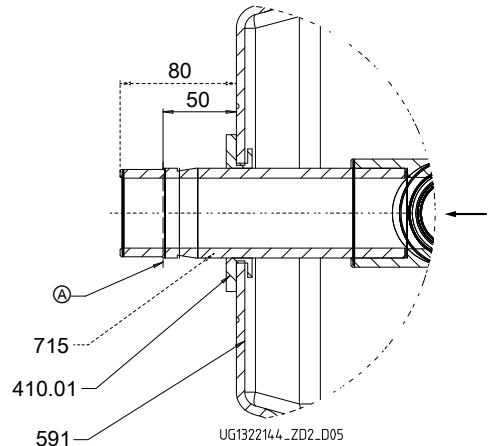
Montaje del tubo en Y y ajuste de la medida de montaje, dimensiones [mm]
